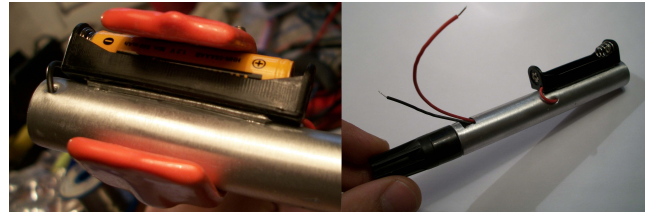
Izq: Detalle de los refuerzos de alambre entre la fuente y el fuste. Dch: la fuente ya fijada.
